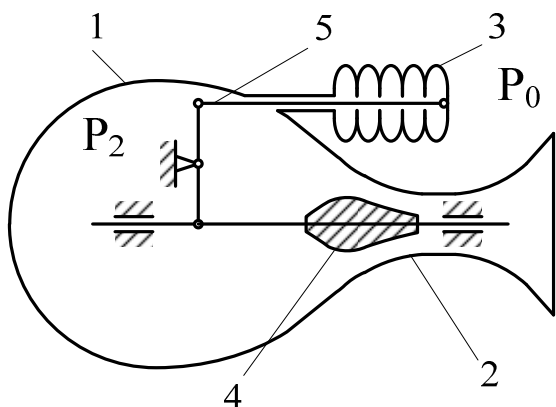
Аналог механічного регулювання форми диффузора, де: 1 – камера; 2 – диффузор; 3 – сильфон; 4 – рухомий шток; 5 – передаточний механізм
